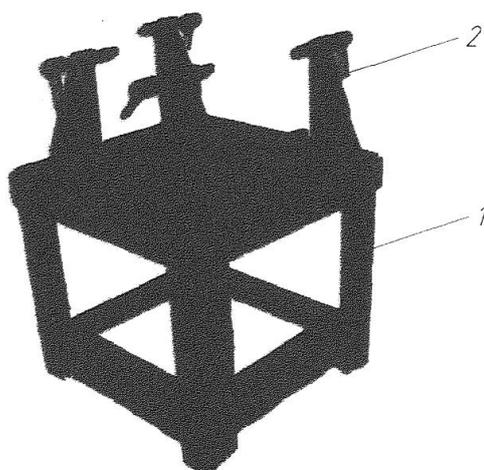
Стенд универсальный для разборки сборки коробок передач грузовых автомобилей модель М-405: 1 – стол; 2 – кронштейн
